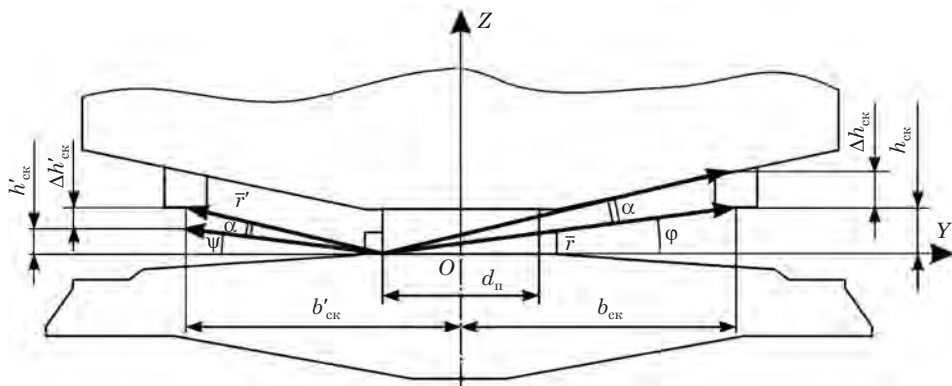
Расчетная схема перевалки кузова на боковую опору
